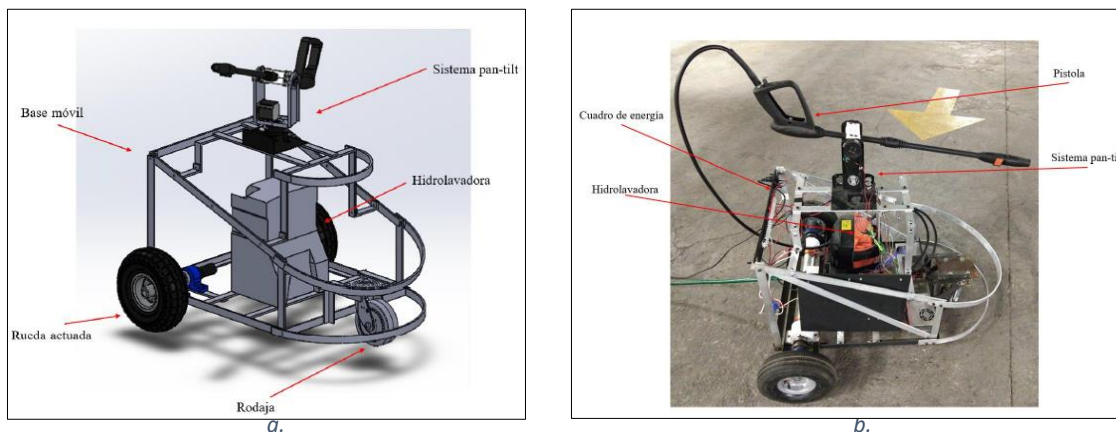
a. Vista isométrica - Diseño CAD; b. Integración del sistema. [23]
